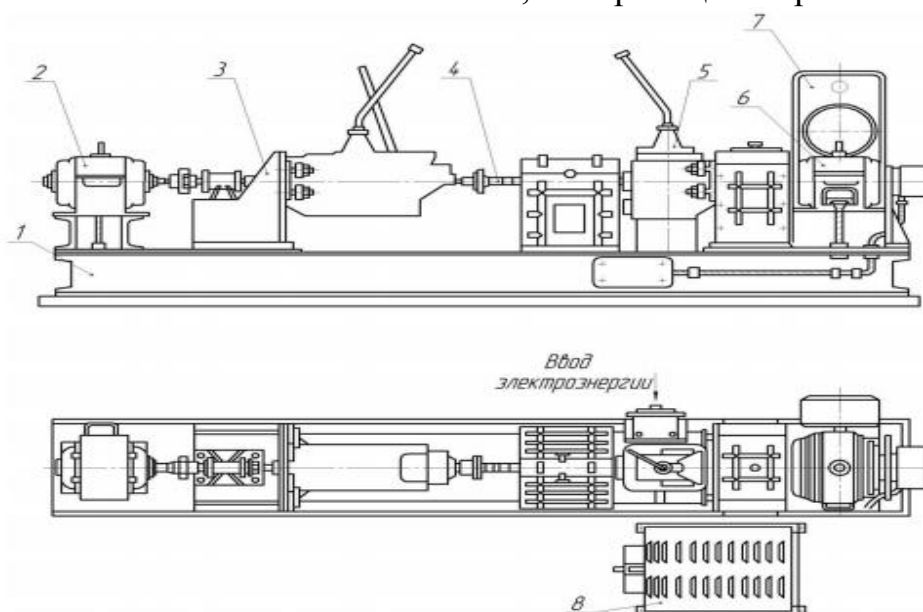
Стенд для испытание коробок передач 5027
